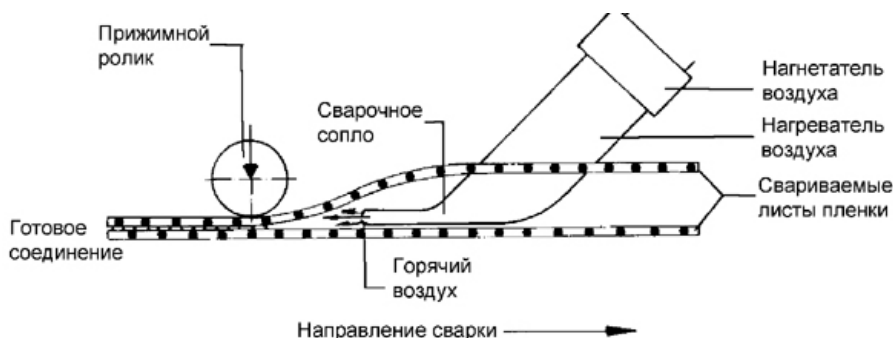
Ручное оборудование для сварки горячим воздухом
